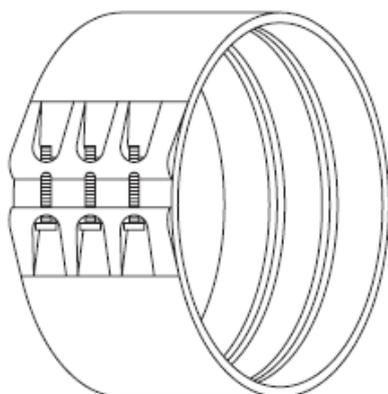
Manguito flexible de acero tipo ARPOL o similar.
